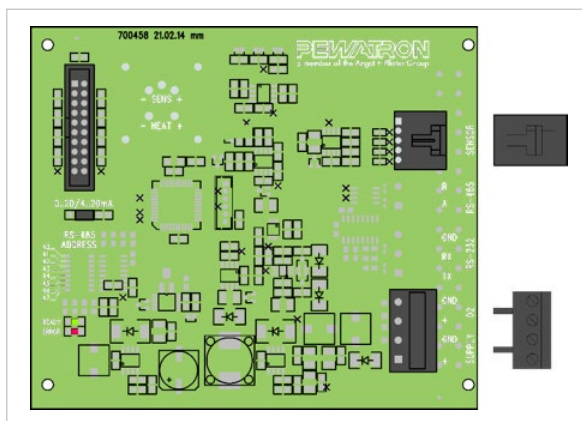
FCX-MCxx-EXT 的 PCB 侧带插头电缆连接器
